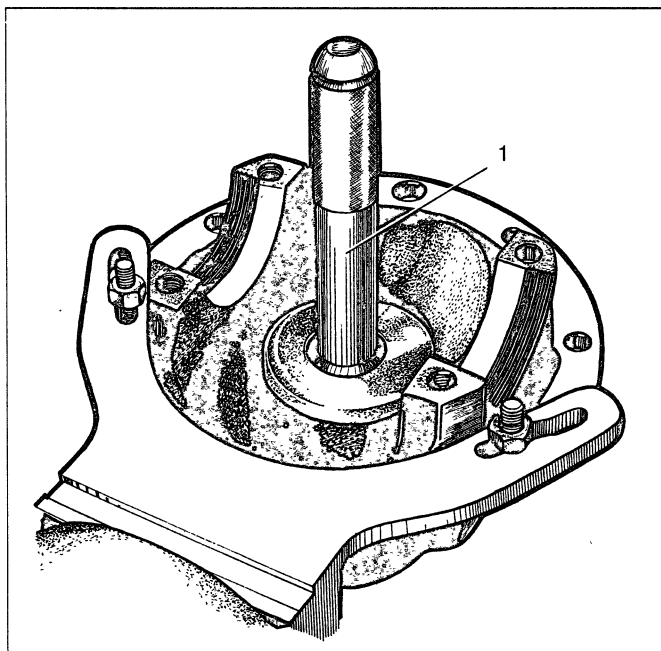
Установка наружного кольца заднего подшипника ведущей шестерни оправкой: 1 – оправка А.70171
